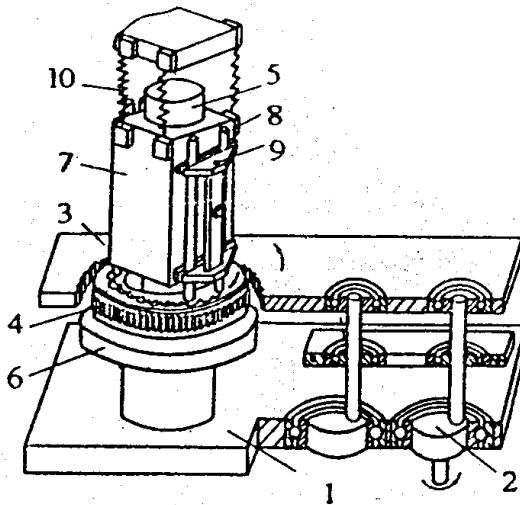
Конструкция станка для доводки плоского торца стержней
